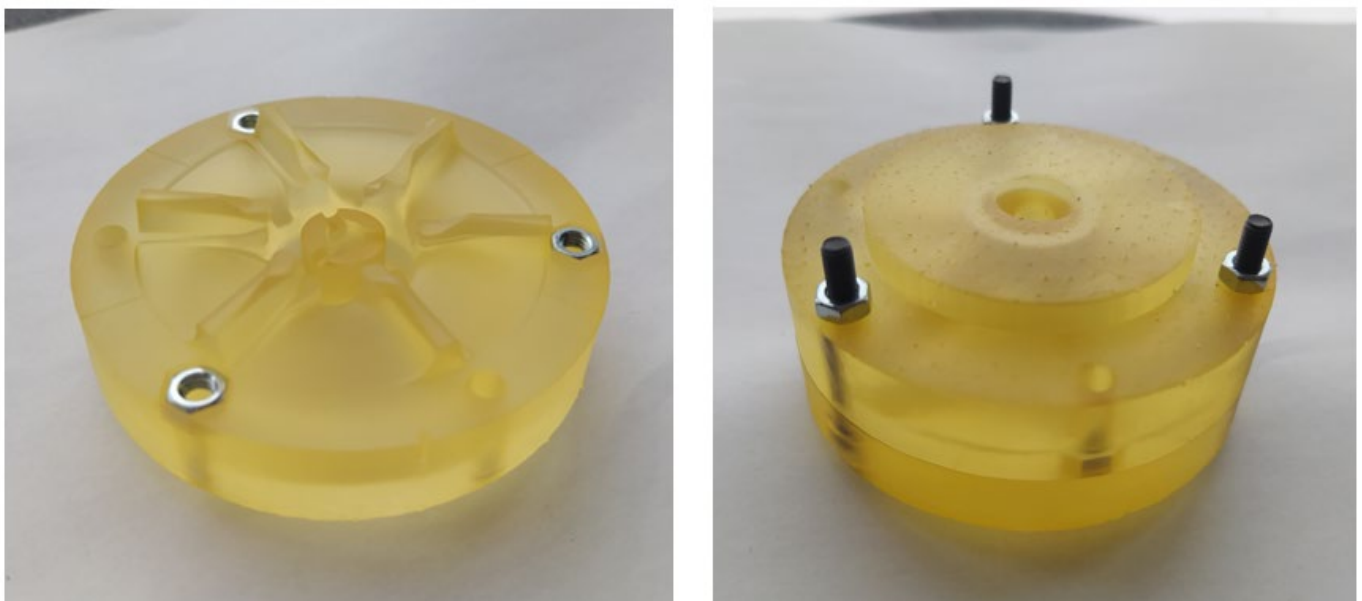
Tuerca para desmoldeo (*izquierda*) y cierre del molde (*derecha*).
